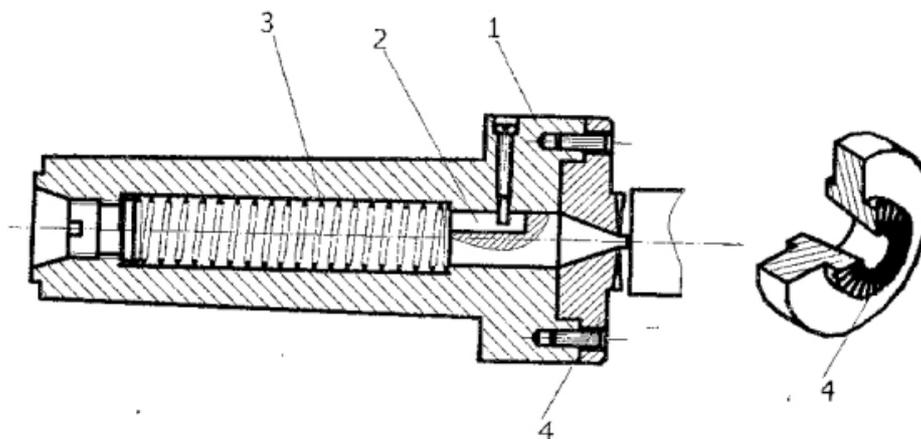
Конструкция поводкового плавающего переднего центра: 1 – корпус; 2 – плавающий центр; 3 – пружина; 4 – сменный зубчатый диск.
